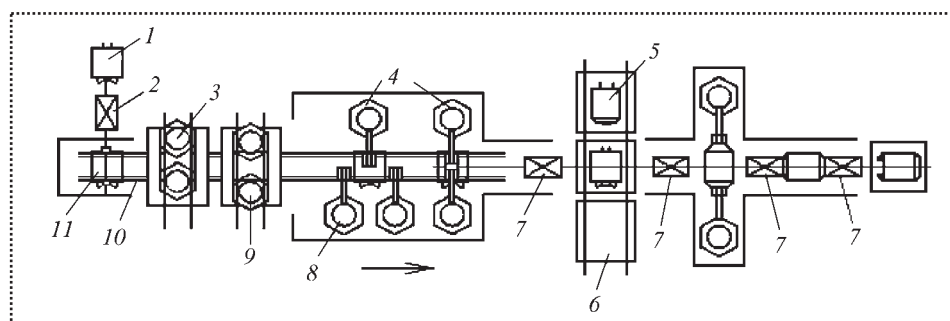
Структура линии сборки-сварки основания кузова:
